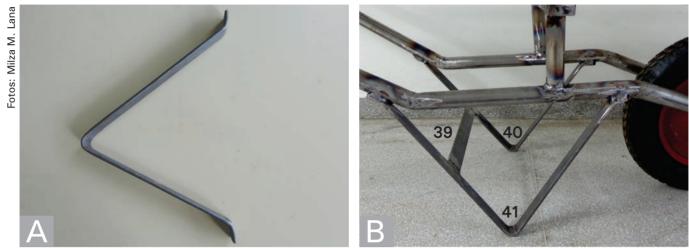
Dobra das extremidades dos pés para facilitar a sua soldagem à base (A) e local de soldagem dos pés (B), Embrapa Hortaliças, 2014.
